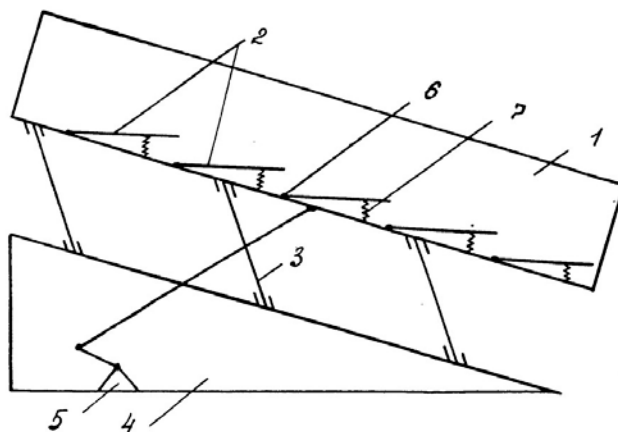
Устройство для смешивания. Общий вид: 1 — виброжелоб; 2 — перемешивающие элементы; 3 — рессоры; 4 — рама; 5 — эксцентриковый привод; 6 — шарниры; 7 — пружины
